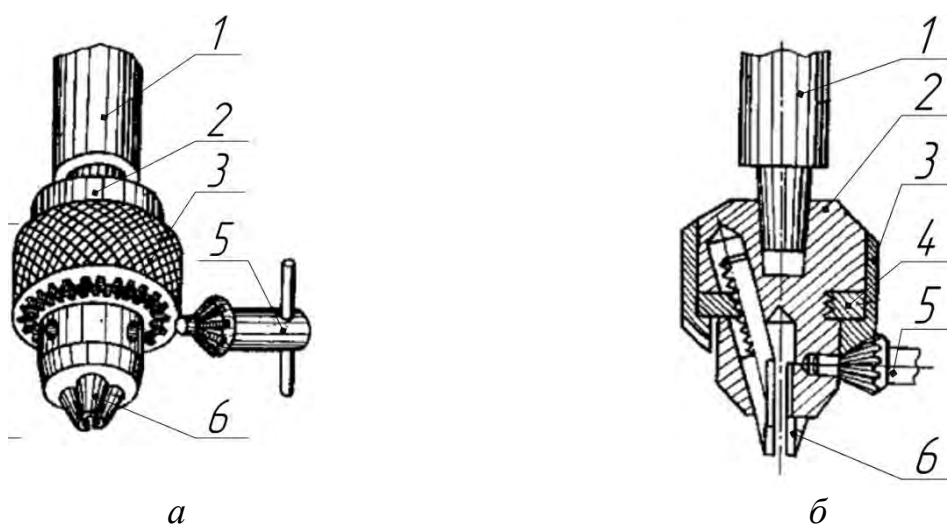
Сверлильный трехкулачковый патрон: а — общий вид; б — разрез
